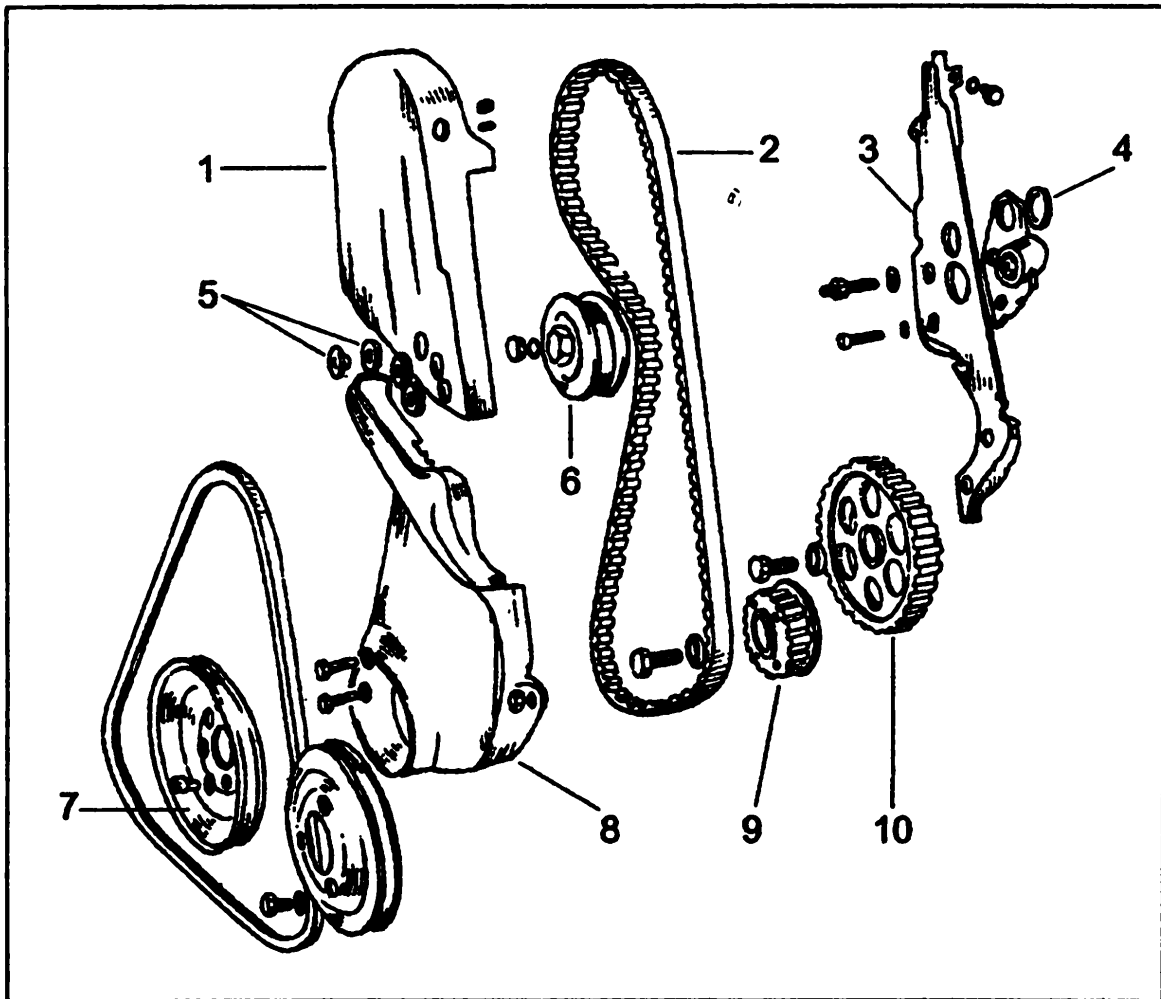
Привод клиновым и зубчатым ремнем в автомобиле «Фольксваген-Пассат»:
